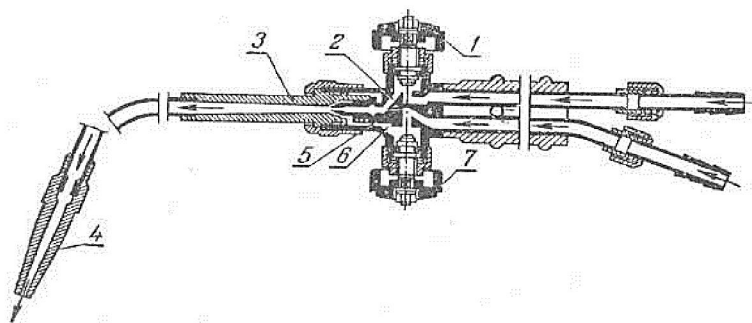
Схема инжекторной сварочной горелки:
